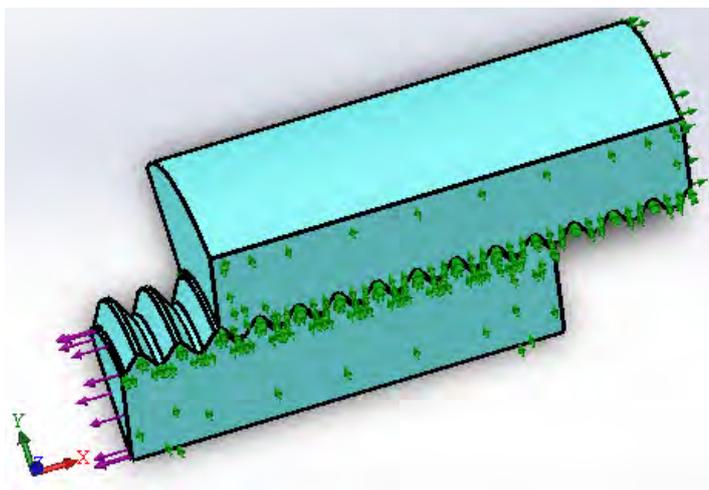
Твердотельная модель резьбового соединения типа стяжки
